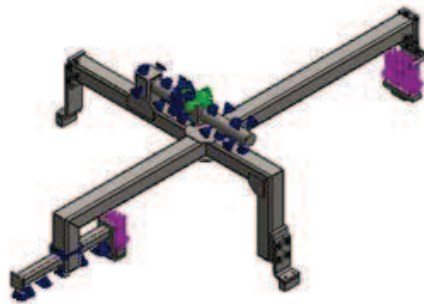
14 Cargas y Restricciones en el Dispositivo de Elevación del Piso Posterior
